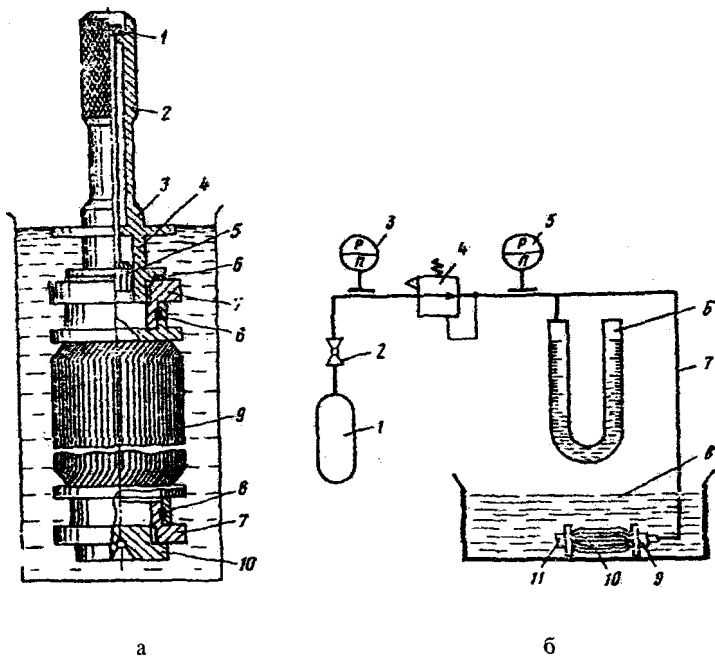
Прибор для проверки чистоты фильтров (а): 1 – сигнализатор заполнения фильтра; 2 – ручка; 3 – корпус; 5 – поплавок; 6, 8 – уплотнительные кольца; 7 – сменный переходник; 9 – проверяемый фильтроэлемент; 10 – заглушка. Гидравлическая схема стенда для проверки фильтрующих элементов на герметичность (б): 1 – баллон со сжатым воздухом; 2 – вентиль; 3 – манометр 0...25 МПа; 4 – редуктор; 5 – манометр 0...0,25 МПа; 6 – пьезометр; 7 – резиновый шланг; 8 – ванночка с бензином; 9 – переходник; 10 – проверяемый фильтроэлемент; 11 – заглушка
